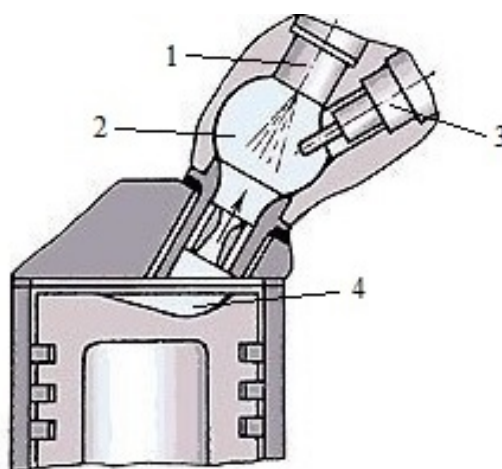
Двигатель с форкамерно-факельным зажиганием [3]:
